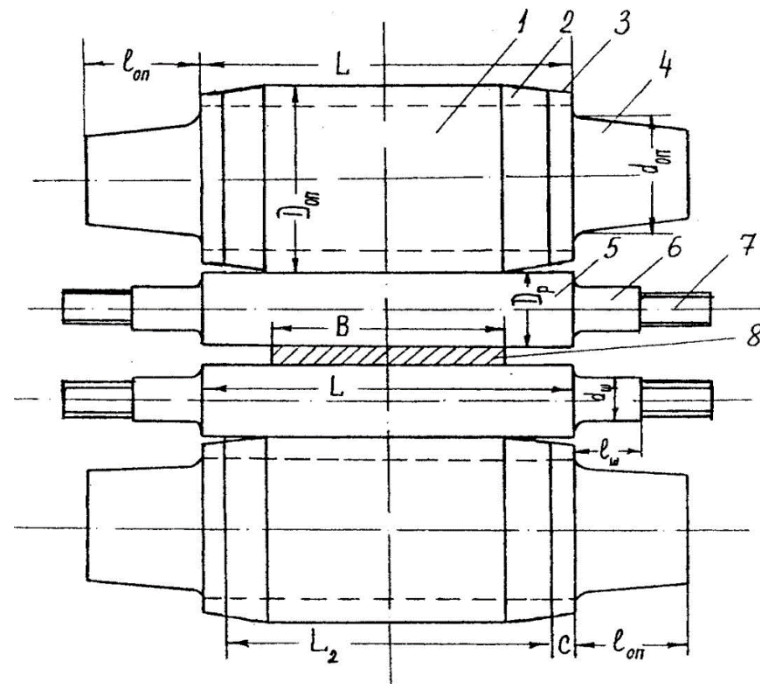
Валковий вузол чотиривалкової кліті: 1- вісь опорного валка; 2 - бандаж; 3 - кінцевий скіс; 4 - шейки опорного валка; 5 - робочий валок; 6 - шейку робочого валка; 7 - хвостовик; 8 - штаба.
